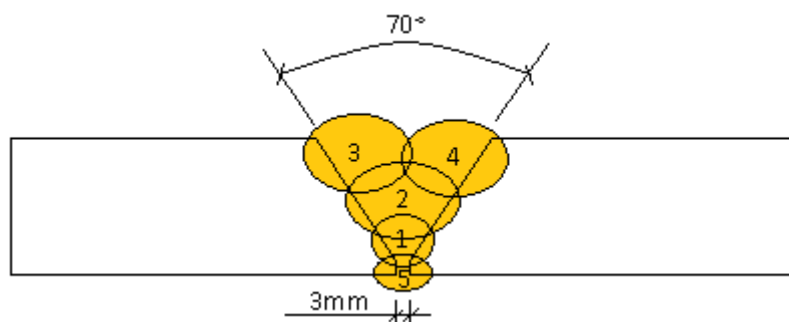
Esquema utilizado na soldagem pelo processo GTAW.
